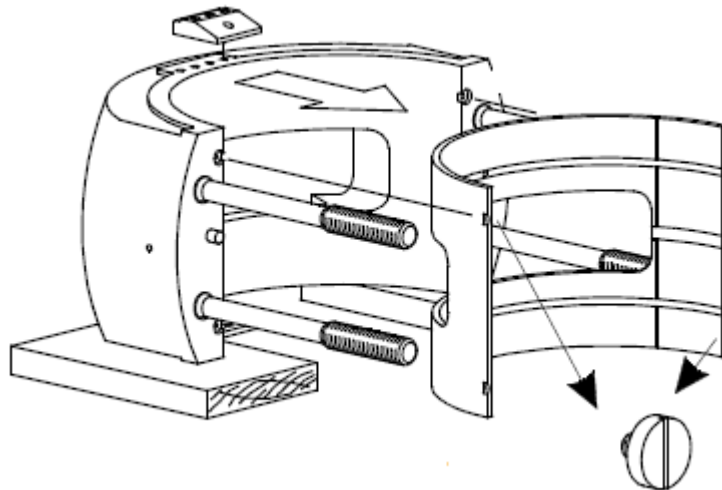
Перевірка вкладиша крейцкопфного підшипника
